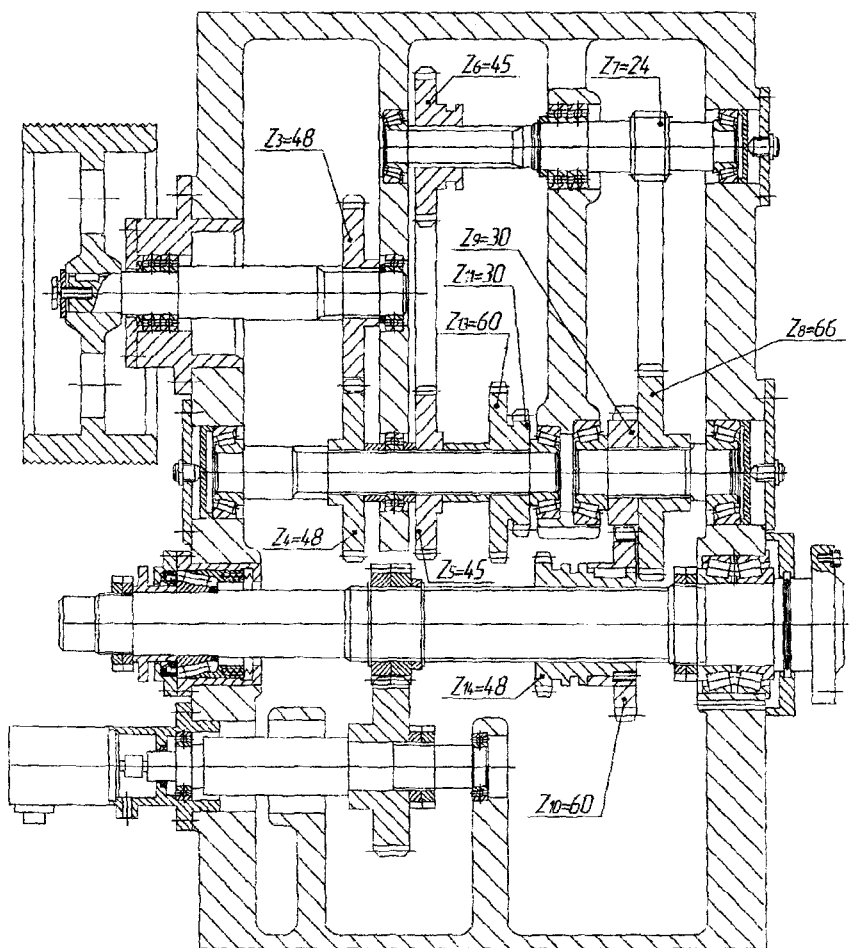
Главный привод токарного станка с ЧПУ модели 16K20Ф3
